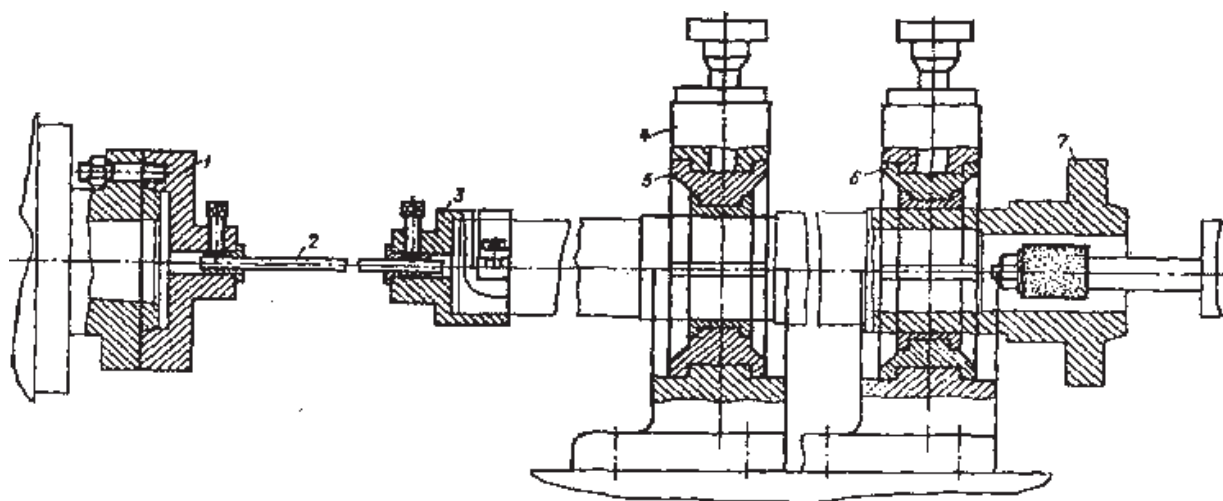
Наладка шлифовального станка с двумя люнетами
